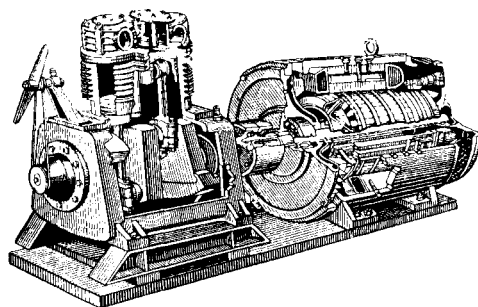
Мотор-компрессор Э-500: 1—корпус компрессора; 2—цилиндр низкого давления; 3—цилиндр высокого давления; 4—прилив для подшипника вала двигателя; 5—гнездо подшипника вала двигателя; 6—крышка картера (корпуса); 7—головка цилиндров; 8, 9—сменные цилиндрические гильзы низкого и высокого давления; 10, 11—поршни низкого и высокого давления; 12, 13—шатун; 14—крышка шатуна; 15—шарнирный болт; 16—коленчатый вал; 17—венец зубчатой передачи; 18—малое зубчатое колесо; 19—гайка малого зубчатого колеса на валу двигателя; 20—подшипник малого зубчатого колеса
